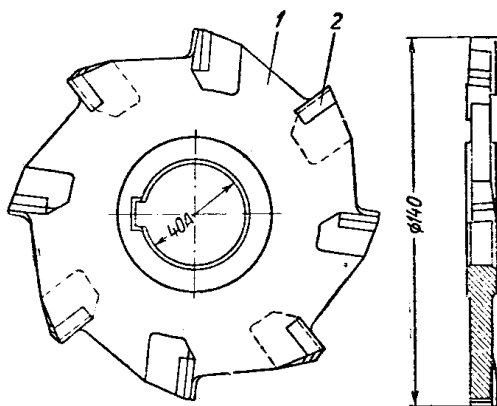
Фасонні фрези з напаяними пластинами з твердого сплаву
